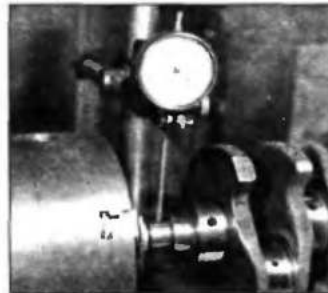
Контроль биения хвостовика вала в неподвижных центрах токарного станка
